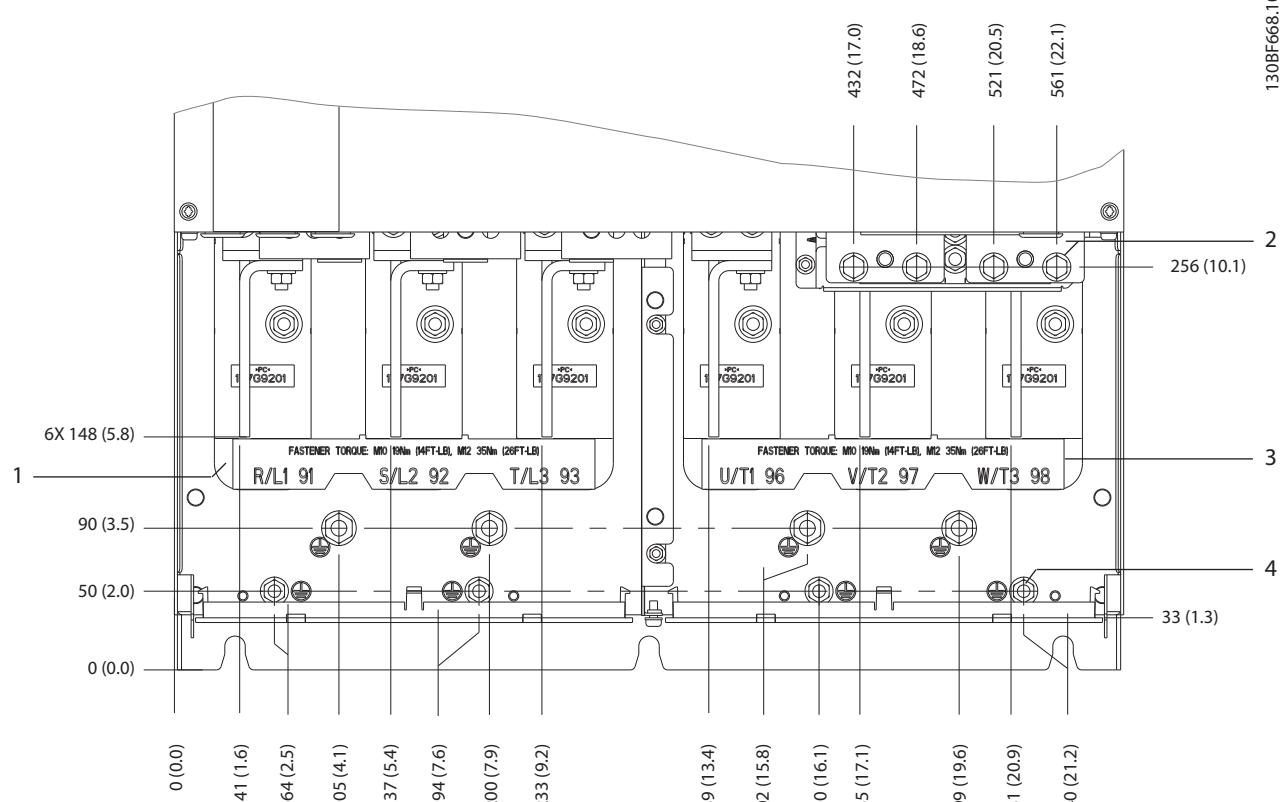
Dimensi Terminal Sumber Listrik, Motor, dan Pemburni E3h (Tampak Samping)
